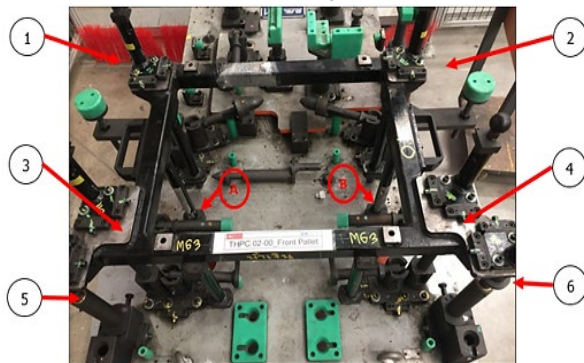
Checking Fixture ของแท่นประกอบชิ้นงาน
